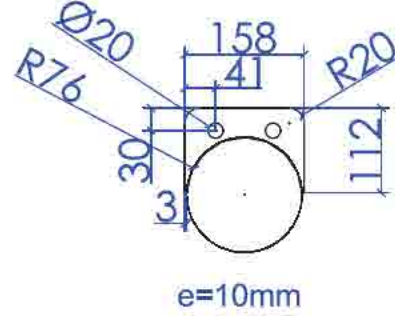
10 (A1) 1:20 (A3)-Cotes en mm
